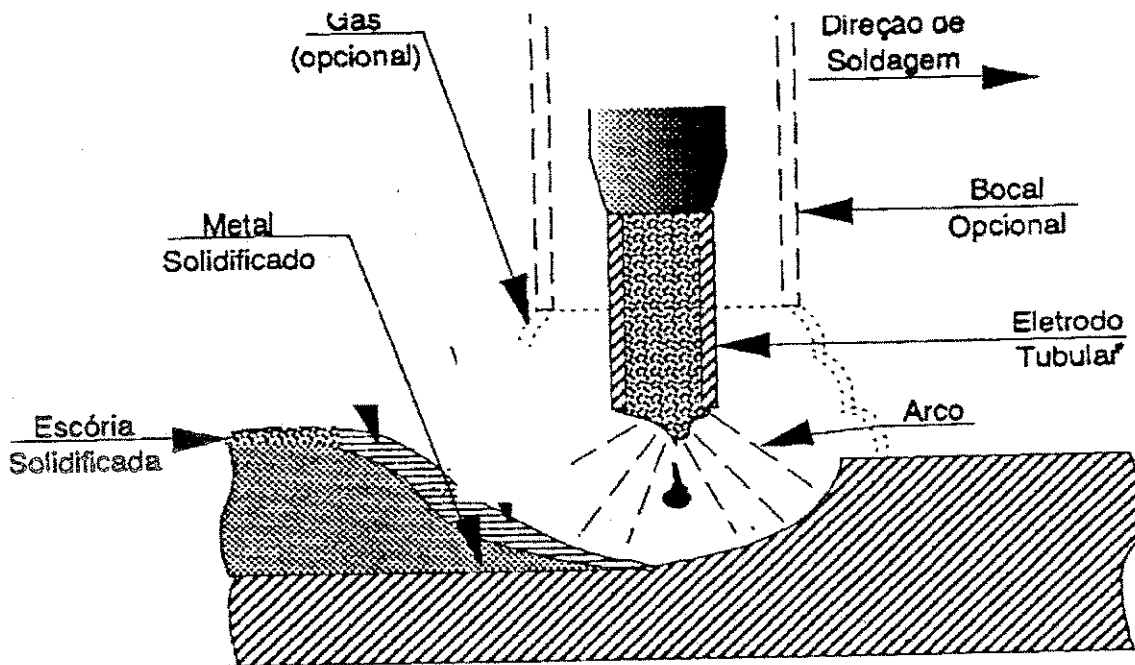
Processo de soldagem a arco com Arame tubular (SAT) (Liu, 1990).
